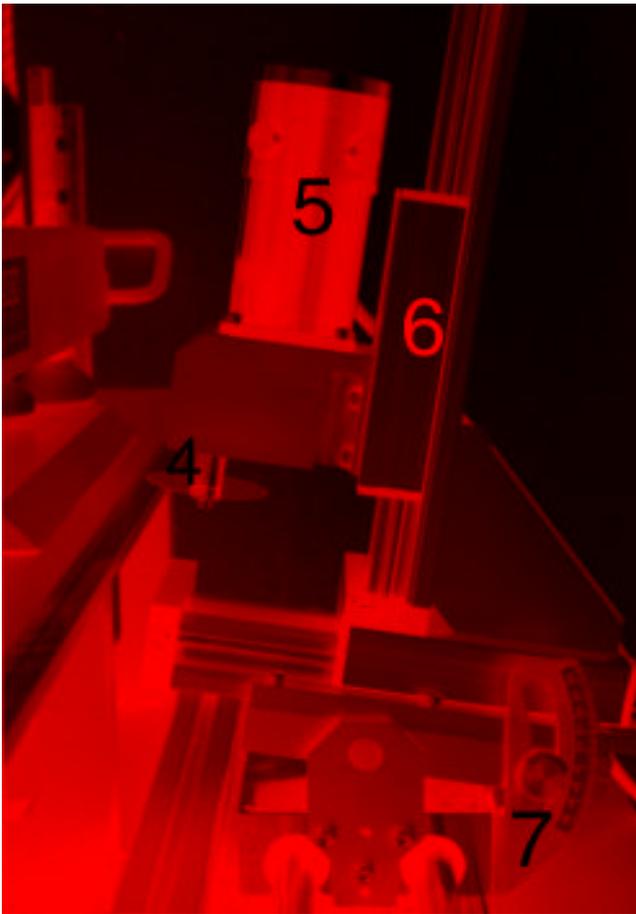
Prototyp der Buchdeckelfräsmaschine, Seitenansicht.
